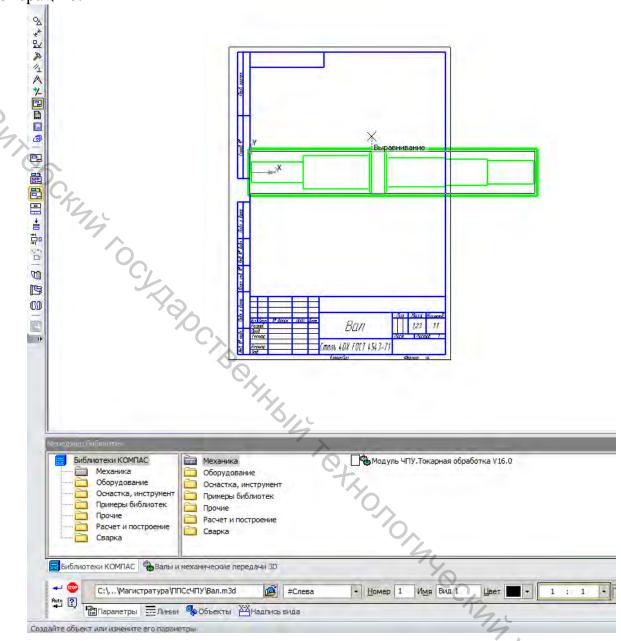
Начальный этап создания рабочего чертежа вала
